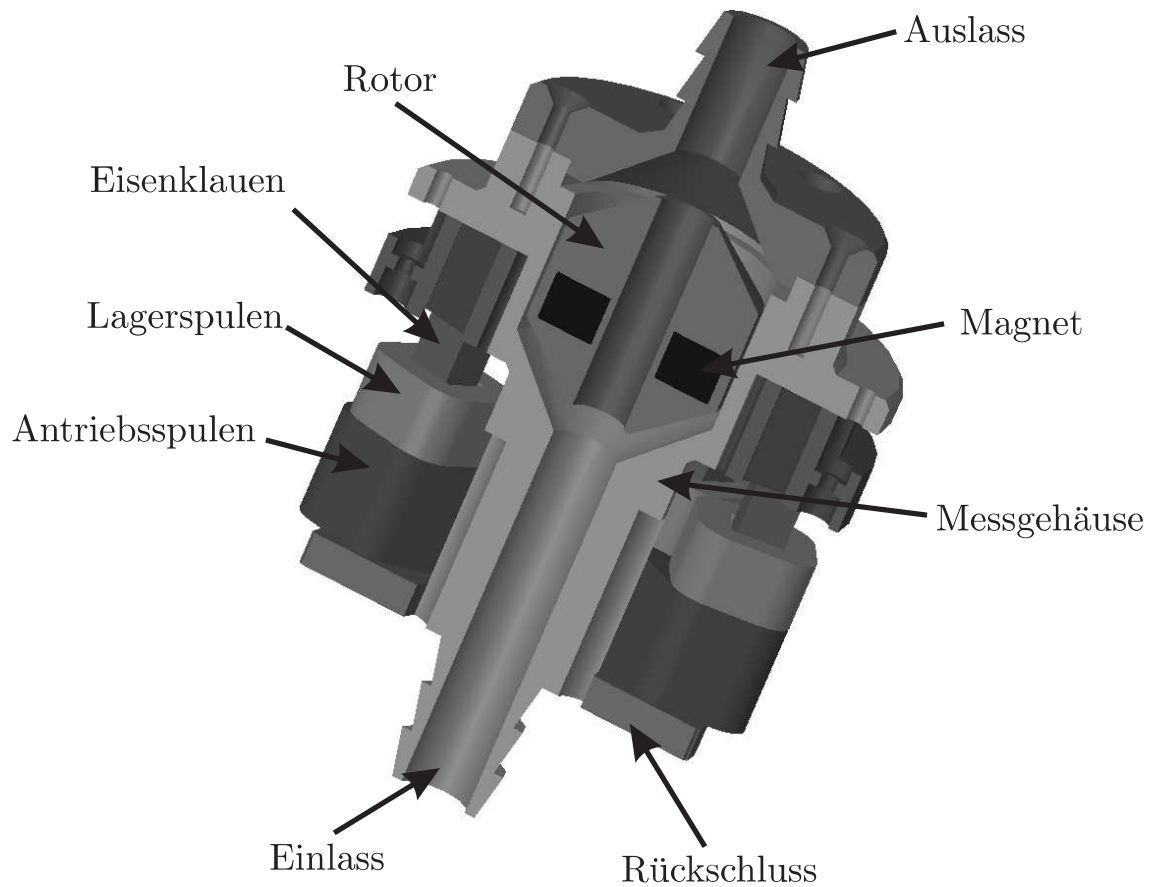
Schnittansicht des Axial-Viskosimeters
